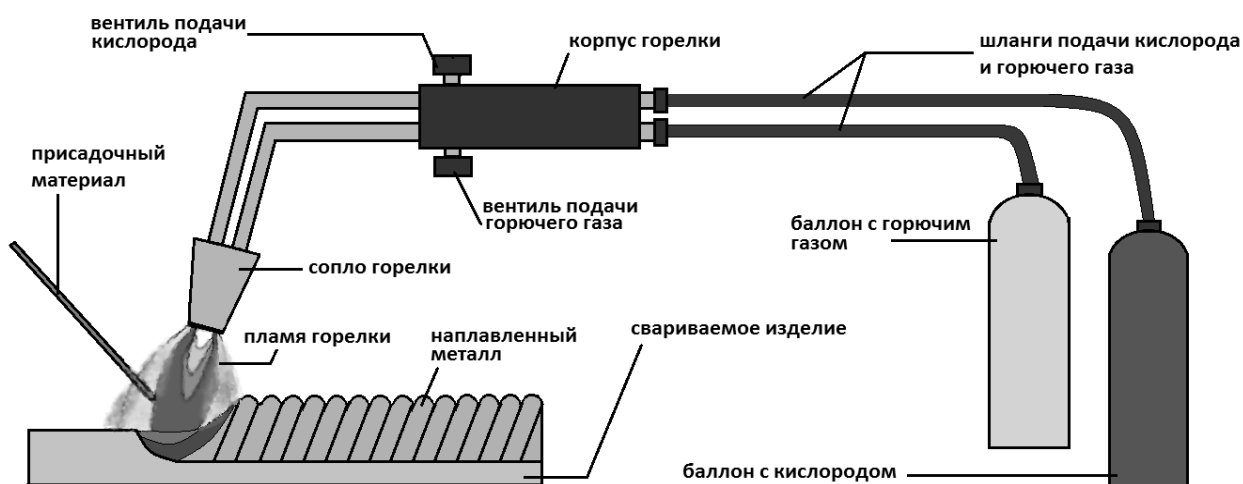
Схема выполнения газовой сварки
